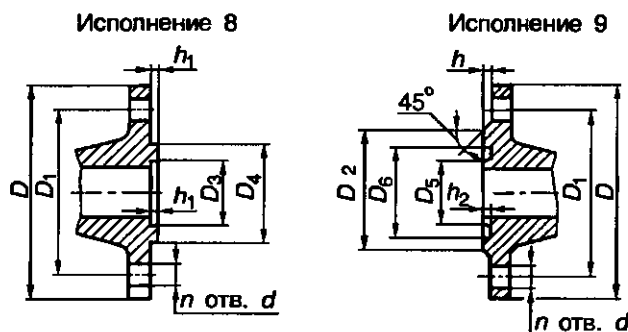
Фланцы под фторопластовую прокладку исполнений: 8 – с шипом; 9 – с пазом
